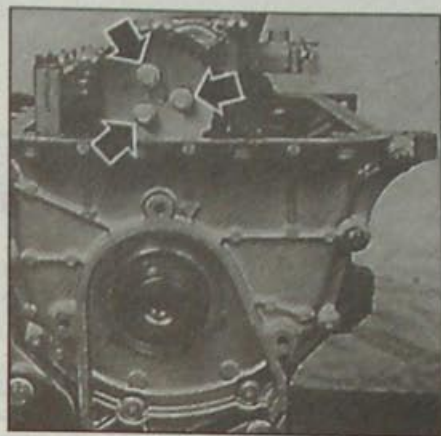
Расположение болтов крепления звездочки масляного насоса
